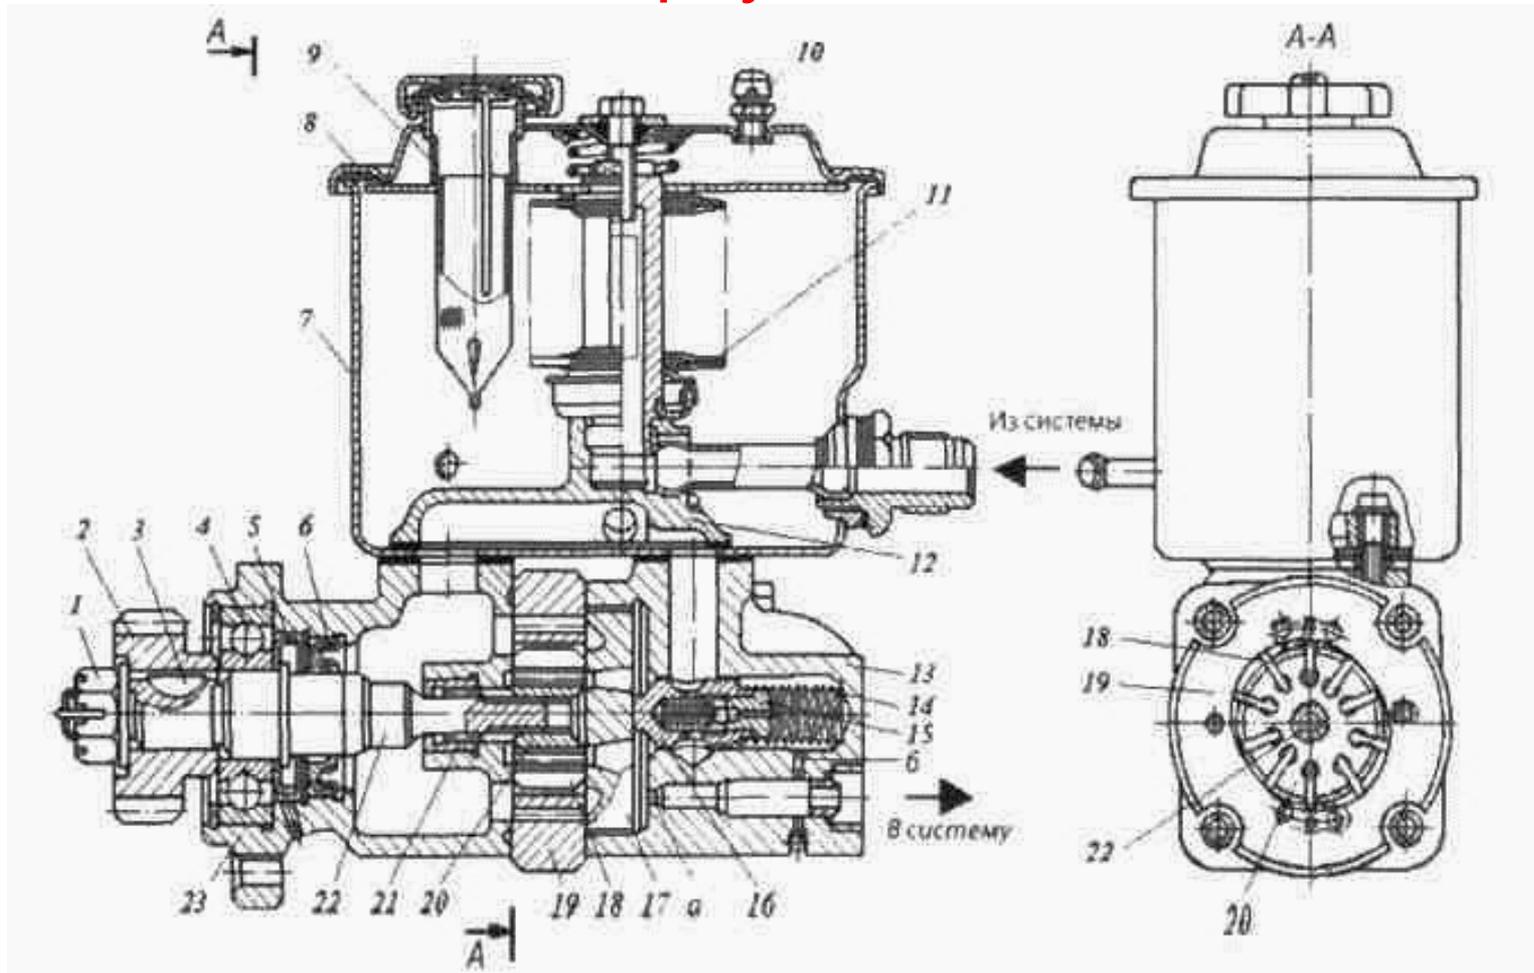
Насос гидравлического усилителя рулевого привода: 1 – гайка; 2 – зубчатое колесо привода; 3 – шпонка; 4, 21 – подшипники; 5 – маслосгонное кольцо; 6 – уплотнительная манжета; 7 – бачок; 8 – крышка бачка; 9 – заливной фильтр; 10 – сапун; 11 – фильтрующий элемент; 12 – коллектор; 13 – крышка; 14 – пружина перепускного клапана; 15 – седло предохранительного клапана; 16 – перепускной клапан в сборе с предохранительным клапаном; 17 – распределительный диск; 18 – лопасть; 19 – статор; 20 – ротор; 22 – вал; 23 – корпус; а и б – дросселирующие отверстия.
